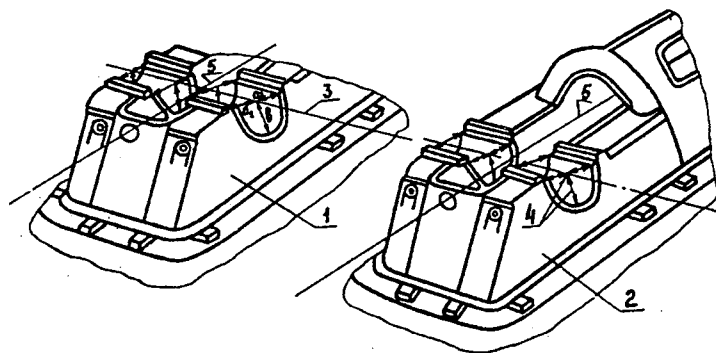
Центровка второй рамы двухрядного горизонтального компрессора по оси вала с помощью струны.
